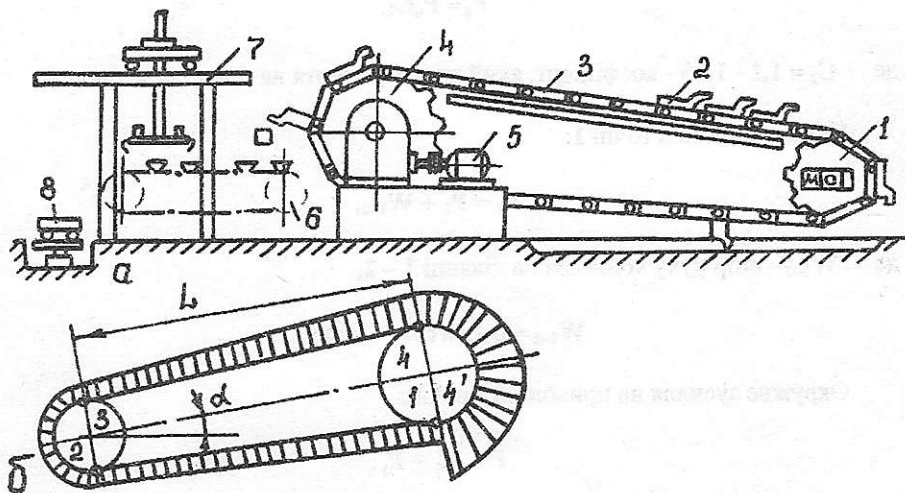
Принципова (а) і розрахункова (б) схеми стрічкової розливної машини: 1, 4 - натяжна і приводна станції; 2-виливниця; 3-ланцюговий конвейєр; 5-привод; 6-конвейєр чушкоукладальника; 7-чушкоукладальник; 8-поворотний стіл
